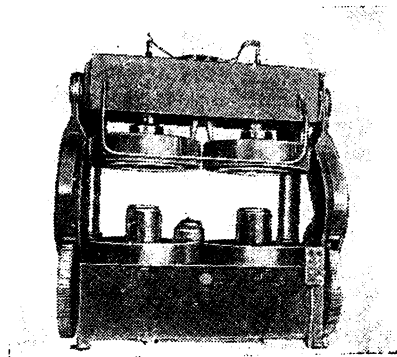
Общий вид форматора-вулканизатора с надетыми на диафрагмы сырыми покрышками.
